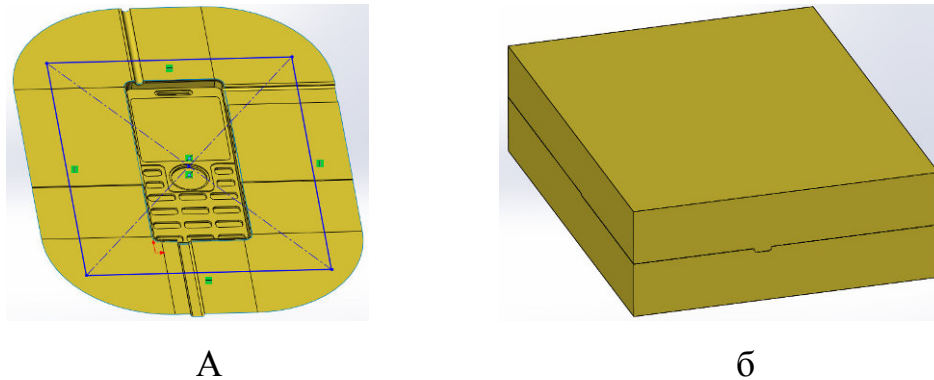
Процес формування прес-форми деталі: а) прямокутний ескіз, що визначає форму і розміри прес-форми; б) блок, що містить в собі пуансон, матрицю і деталь
